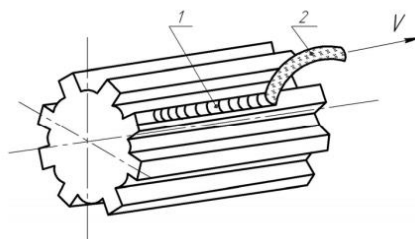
Схема продольной наплавки шлицевой поверхности детали: 1 – наплавленный слой; 2 – электродная проволока
